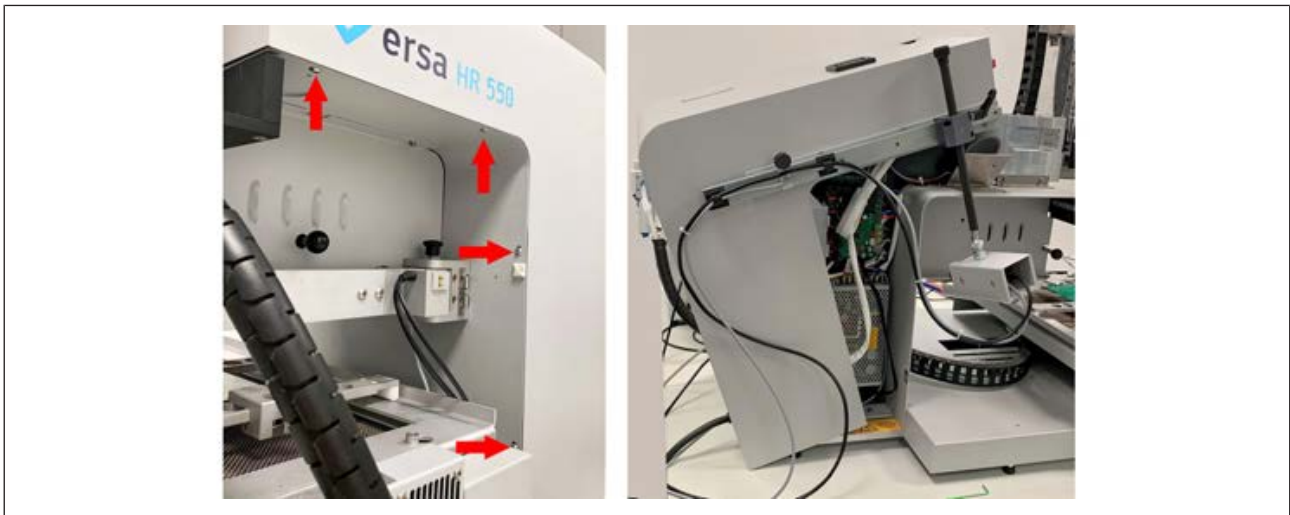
Desserrer les quatre vis de chaque côté et ouvrir le boîtier vers l'arrière
